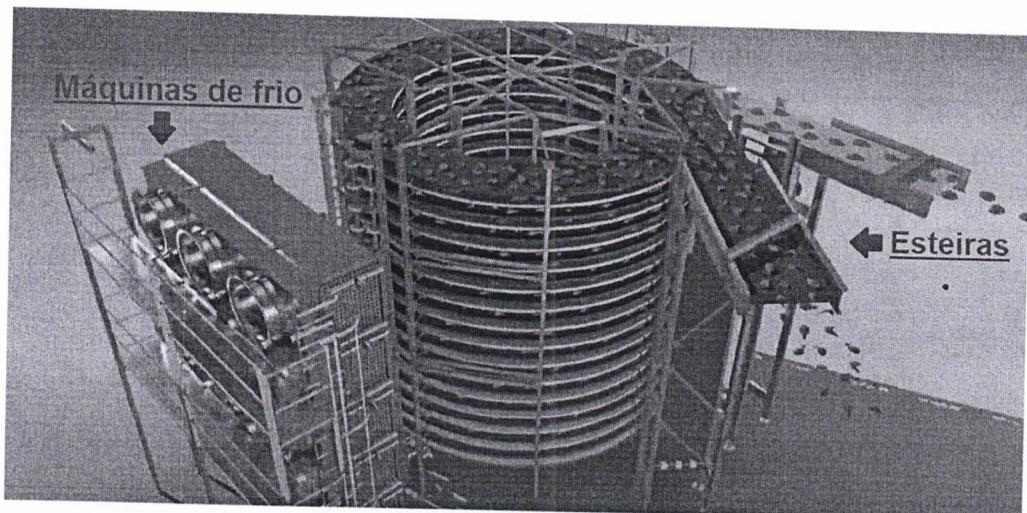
Vista 1 Estrutura tecnológica de esteiras e máquinas de frio para IQF
